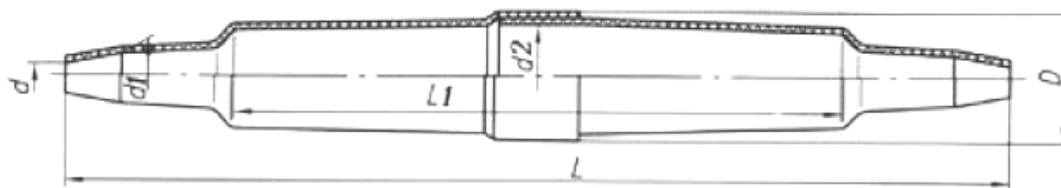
Размеры муфты МПП с корпусом из двух деталей, полумуфт.
